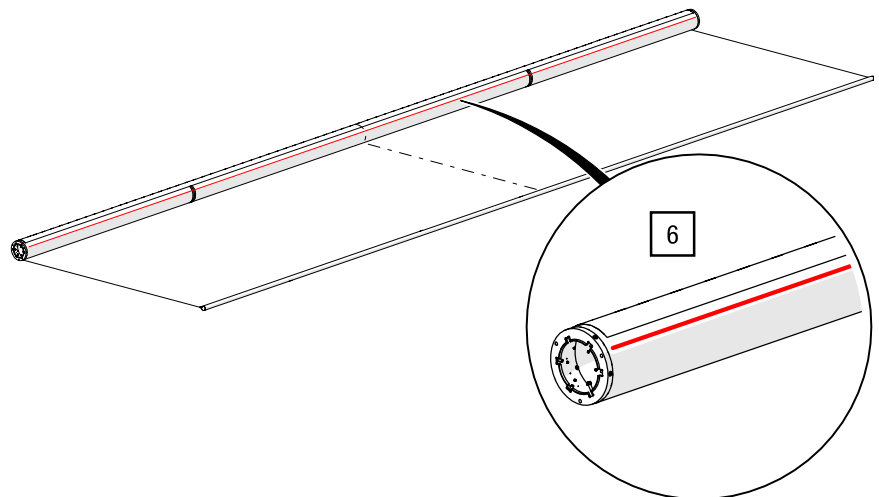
Behang Montieren – Markierung mit Schlagseil achsparallel hinzufügen
